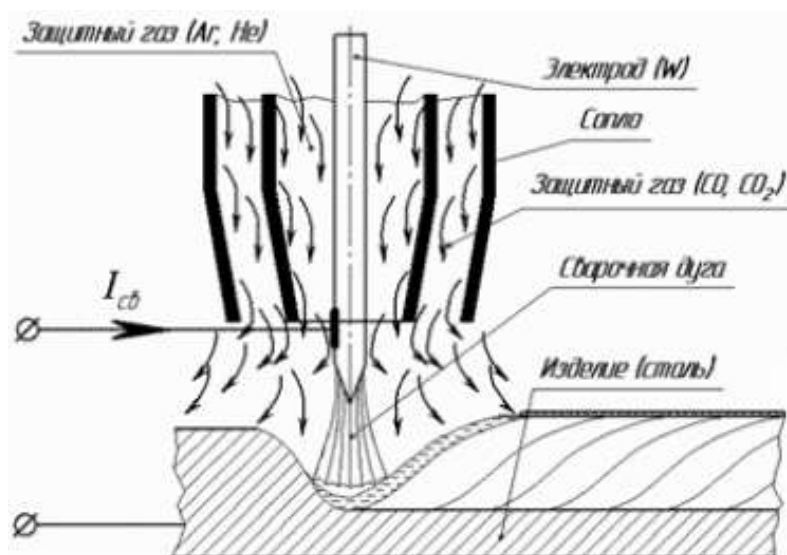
Схема сварки неплавящимся электродом с комбинированной защитой
